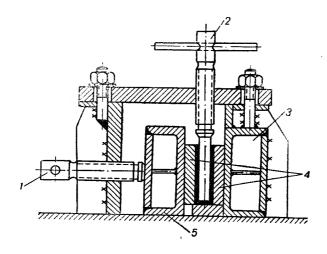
Паровая пресс-форма для опрессовки роторных гильз:
